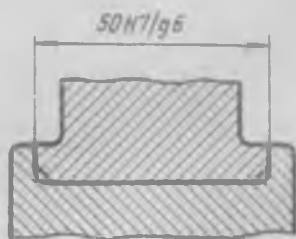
Приемы нанесения допусков на сборочных чертежах
